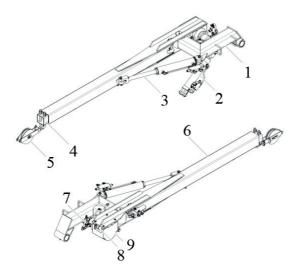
Стрела манипулирования штангами: 1 – поворотная консоль; 2 – вертикальный цилиндр; 3 – боковой цилиндр; 4 – удлинитель стрелы штанги; 5 – шкив; 6 – стойка стрелы штанги; 7 – гидравлика лебедки штанги; 8 – трос лебедки штанги; 9 – лебедка штанги
